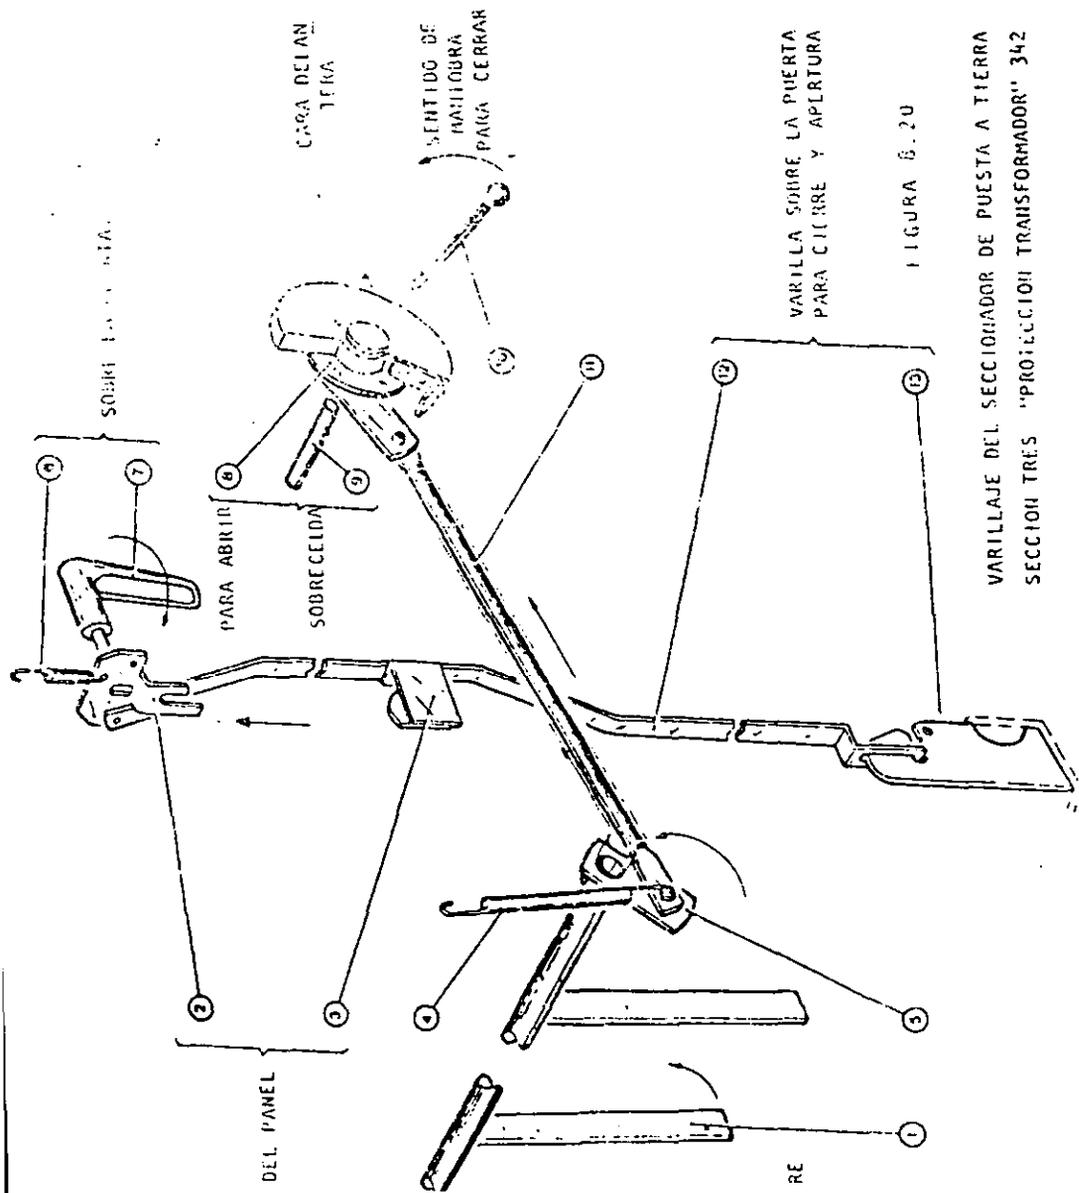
Varillaje del Seccionador de Puesta a Tierra, Sección Tres. "Protección a Transformador 342".
